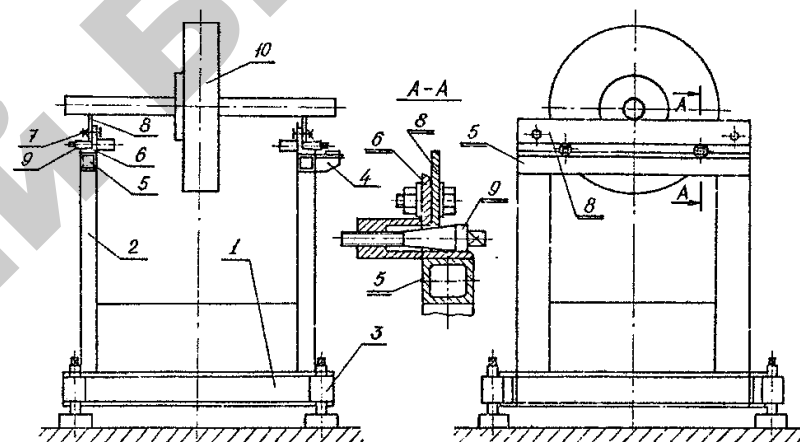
Схема лабораторного стенда для статической балансировки роторов: 1 – основание; 2 – стойка; 3 – винтовая опора; 4 – пузырьковый уровень; 5 – перекладина; 6 – планка; 7 – болты крепления; 8 – ножи; 9 – винты регулировочные; 10 – ротор
